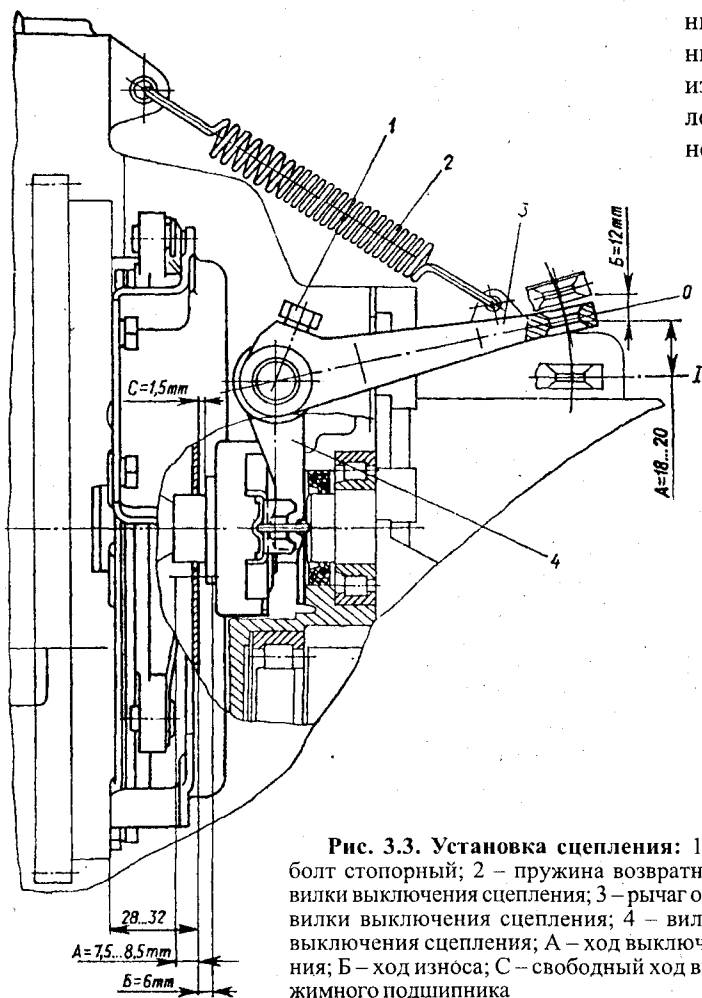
Установка сцепления: 1 – болт стопорный; 2 – пружина возвратная вилки выключения сцепления; 3 – рычаг оси вилки выключения сцепления; 4 – вилка выключения сцепления; А – ход выключения; В – ход износа; С – свободный ход выжимного подшипника
